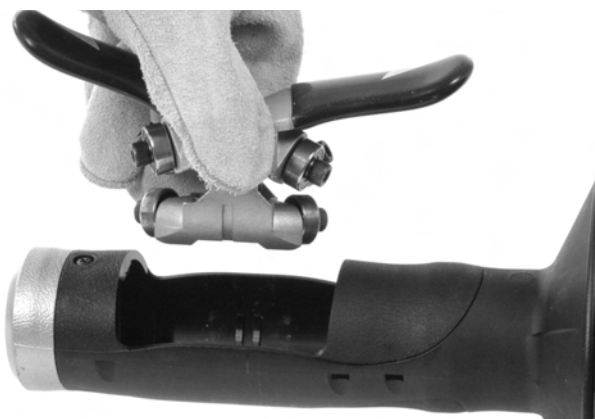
B – Снятие механизма автоподачи AUTOFEED с корпуса
